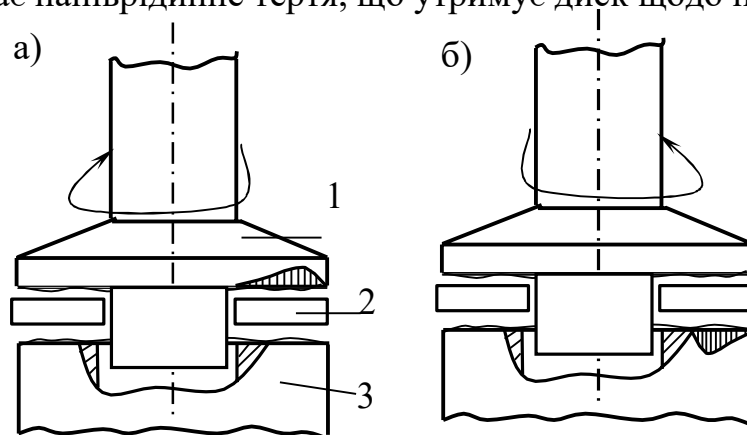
Реверсивний упорний ПК із проміжним плаваючим диском: 1 – п'ята; 2 – плаваючий диск; 3 – корпус турбокомпресора
